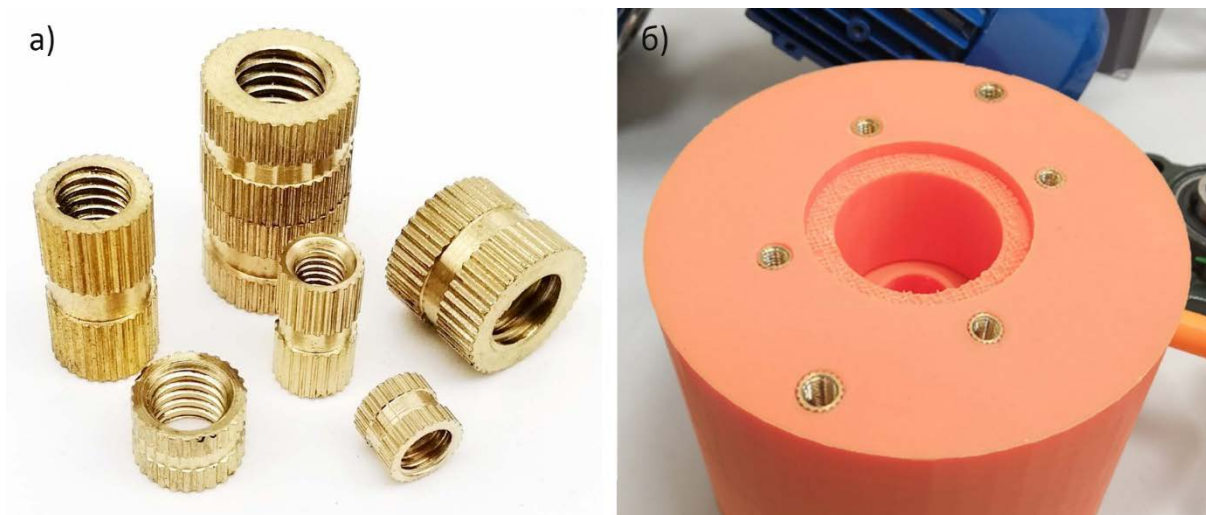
а) Гайки для 3д-принтера; б) деталь с помещенными в неё гайками
